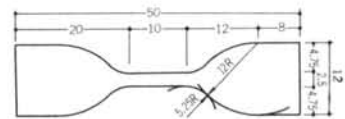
ダンベル型試験体の形状・寸法（単位：mm）
